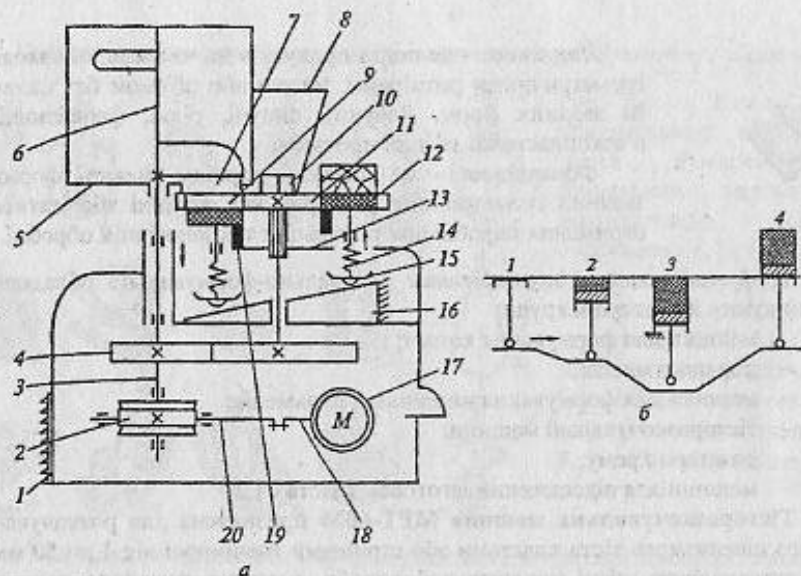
Котлетоформувальна машина МФК-2240: а – схема принципова; б – циклограма руху поршня формувального столу; 1 – корпус; 2 – черв'ячний редуктор; 3 – вал шнека-живильника; 4 – передача циліндрична; 5 – бункер для фаршу; 6 – шнек-живильник; 7 – отвір бункера; 8 – бункер для сухарів; 9 – отвір-чарунка; 10 – гвинт регулювальний; 11 – стіл формувальний; 12 – поршень; 13 – планка; 14 – пружини; 15 – штовхач; 16 – копір торцевий; 17 – електродвигун; 18 – вал електродвигуна; 19 – упор; 20 – вал черв'ячного редуктора
